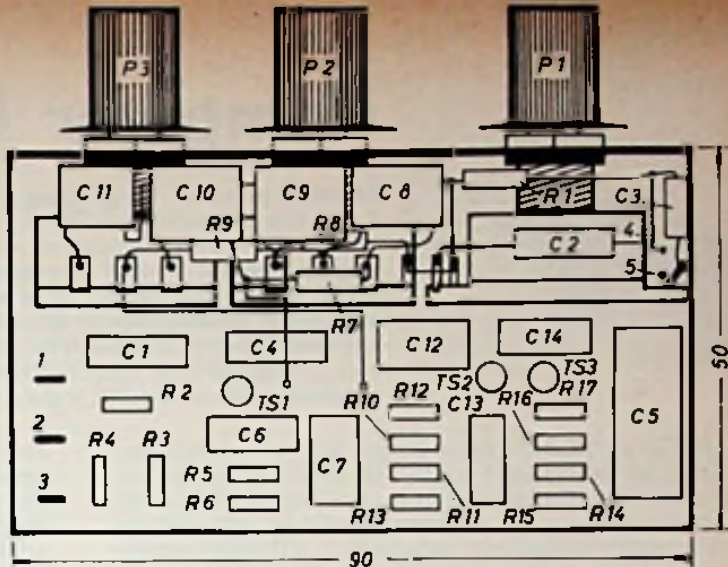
Lay-out van het montagevlak, voor een kruisingsvrije bedrading.
